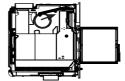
Assemblage de la pierre latérale avant haut droite (H4-22) avec la pierre de raccord (H2-10), conformément au type de raccordement.
